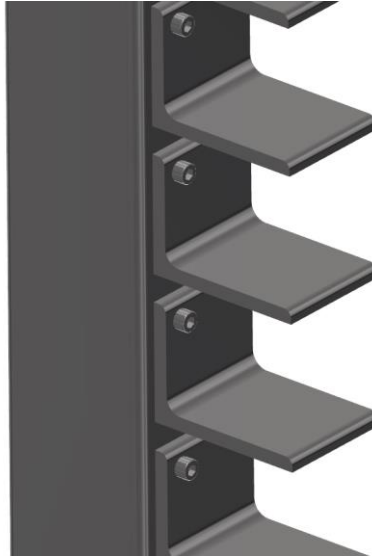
Detailweergave onderkant bewegende hoofdframe
